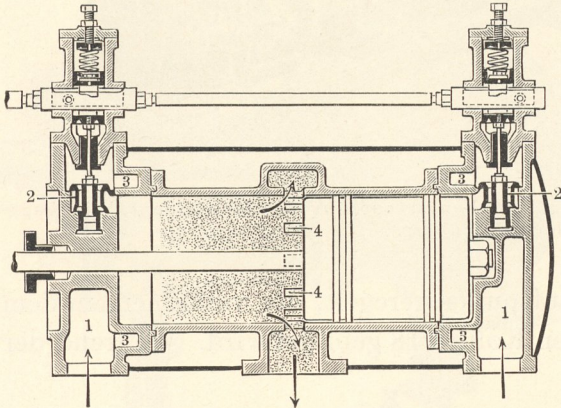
Zylinder der Gleichstromdampfmaschine.
